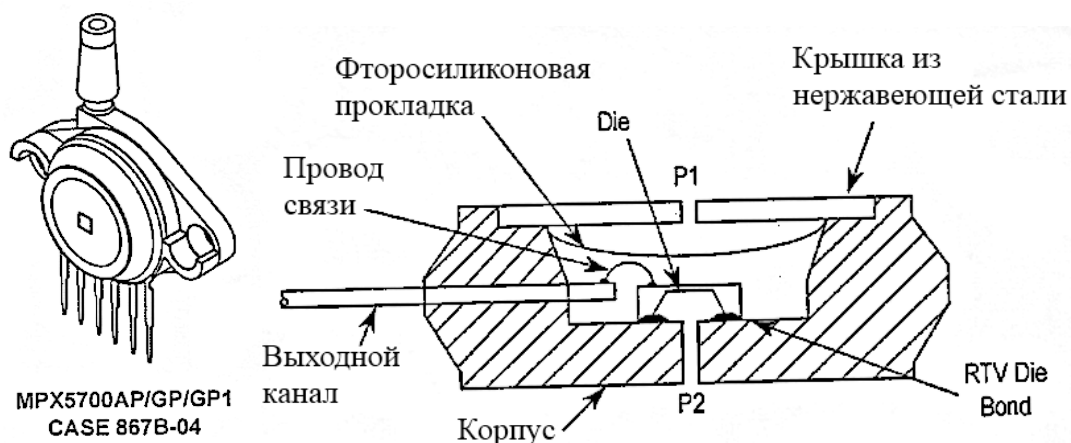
Внешний вид (а) и устройство (б) сенсорного датчика давления
